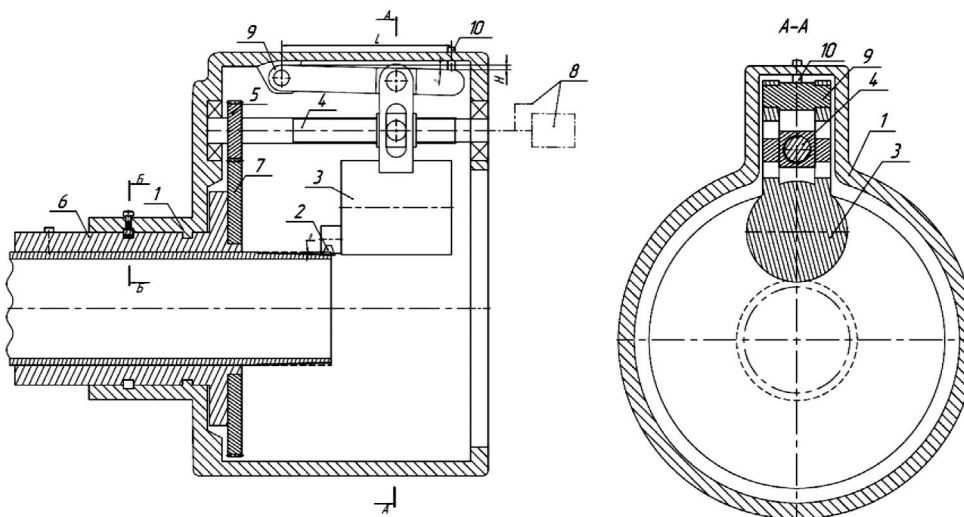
Устройство для нарезания резьб на трубах в устье скважин, где: 1 – корпус устройства; 2 – механизм вращения и подачи режущего инструмента; 3 – электродвигатель; 4 – ходовой винт; 5 – малое зубчатое колесо; 6 – гильза; 7 – большое зубчатое колесо; 8 – привод вращения устройства; 9 – планка регулировки наклона движения; 10 – установочный винт
